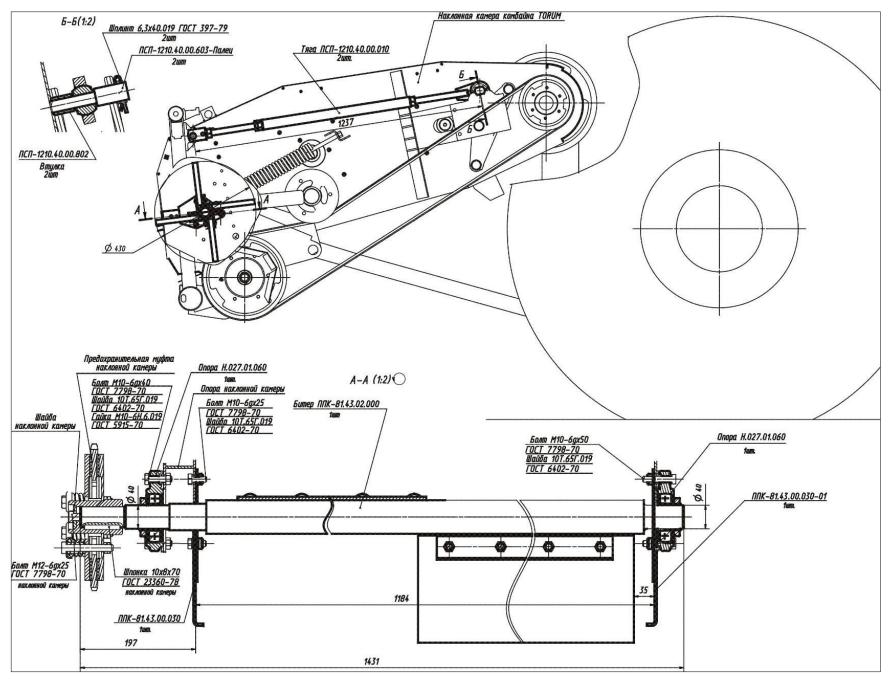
Установка битера приспособления ППК-870-11
